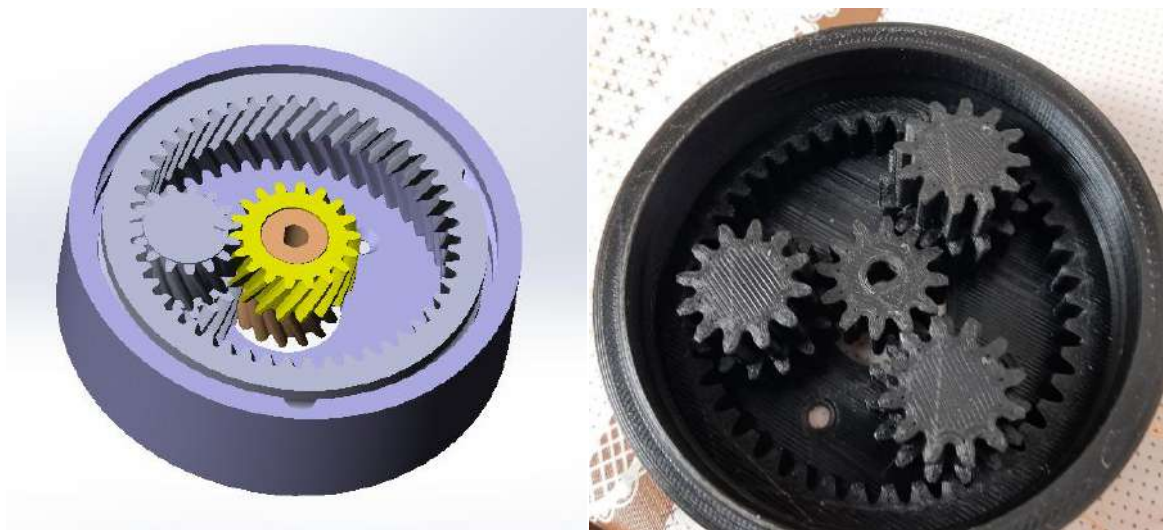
3D-модель и напечатанный вариант планетарного редуктора
